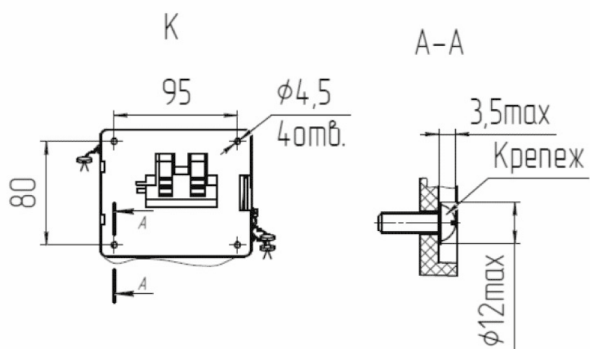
Присоединительные размеры монтажной пластины крепление на стену
